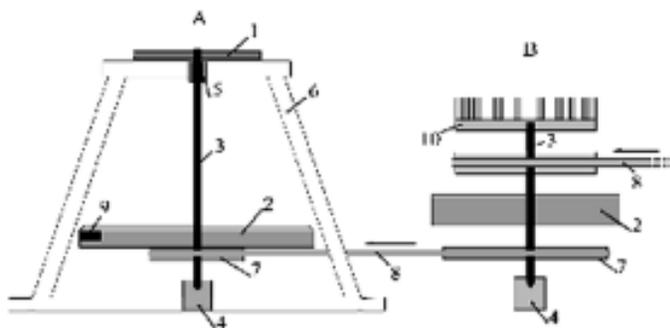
Кинематическая схема гончарного круга с внешним приводом. А - гончарный круг, В - распределитель. 1-формовочный диск, 2-маховик, 3-ось, 4-упорный подшипник, 5-верхний подшипник скольжения, 6-станина, 7-шкив, 8-ремень, 9-противовес, 10-регулятор вращения.
